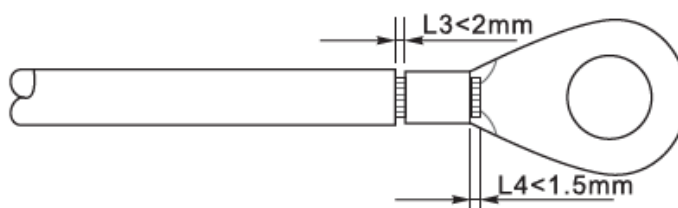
Przygotowanie przewodu uziemienia (2)
